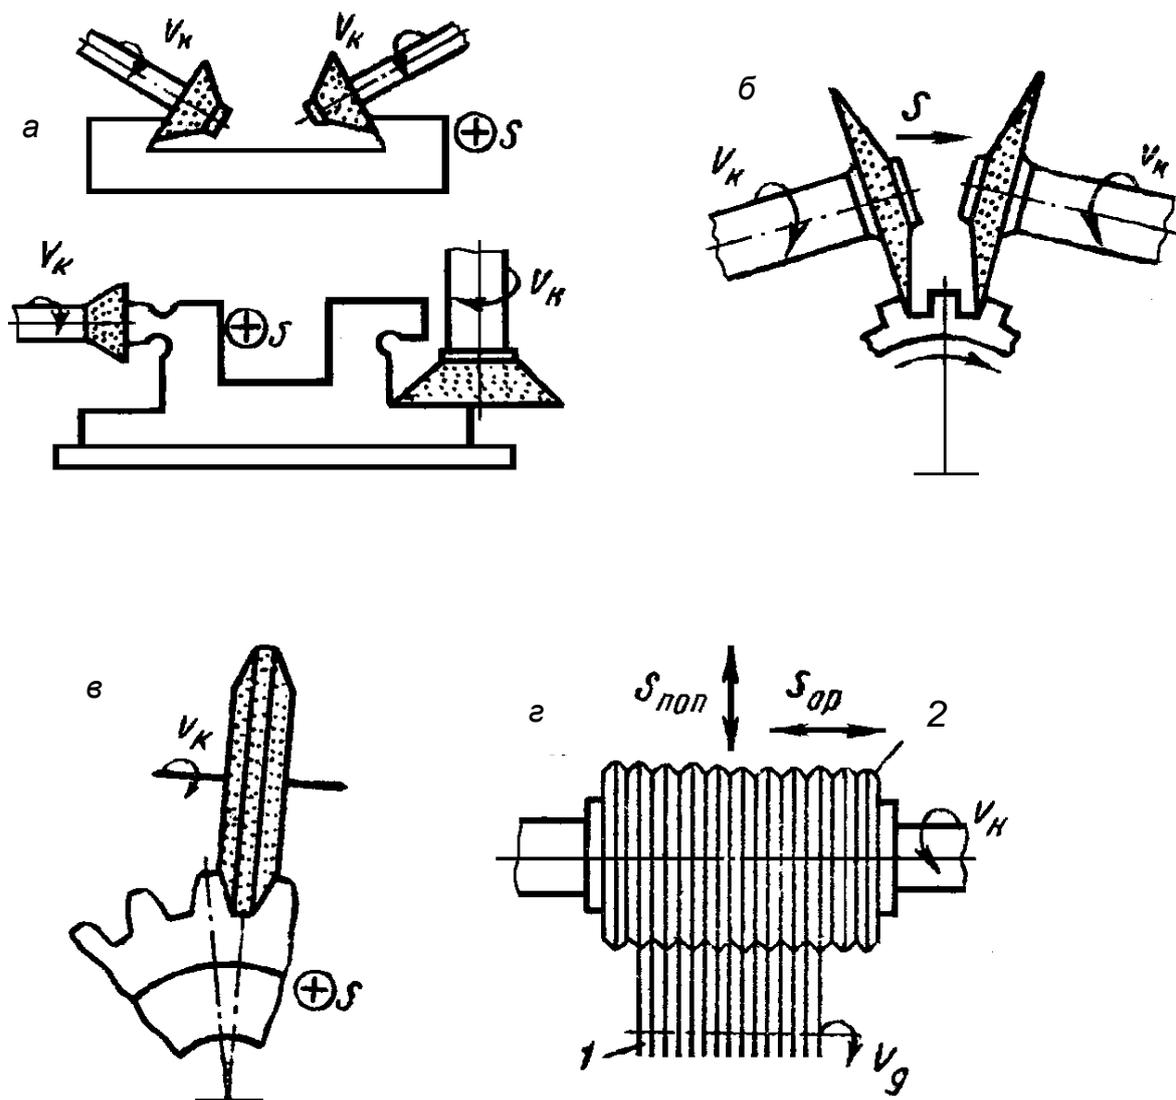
Основные виды шлифования фасонных поверхностей, зубчатых колес и резьбы: а – обработка направляющих станин сложной формы; б – шлифование тарельчатыми кругами; в – профильное копирование; г – отделка резьбы; 1 – деталь; 2 – шлифовальный круг
